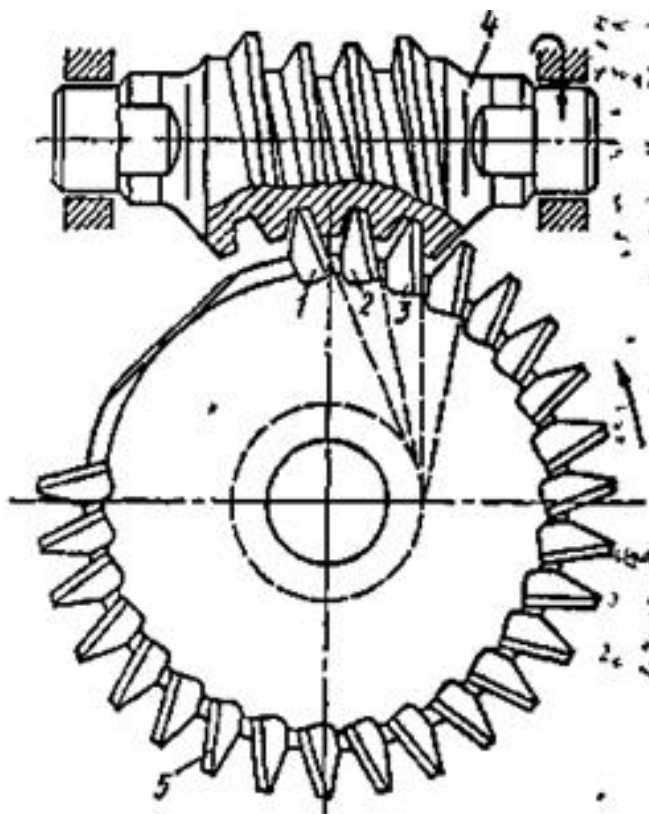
Чистовое нарезание червяка многозубой резцовой головкой
